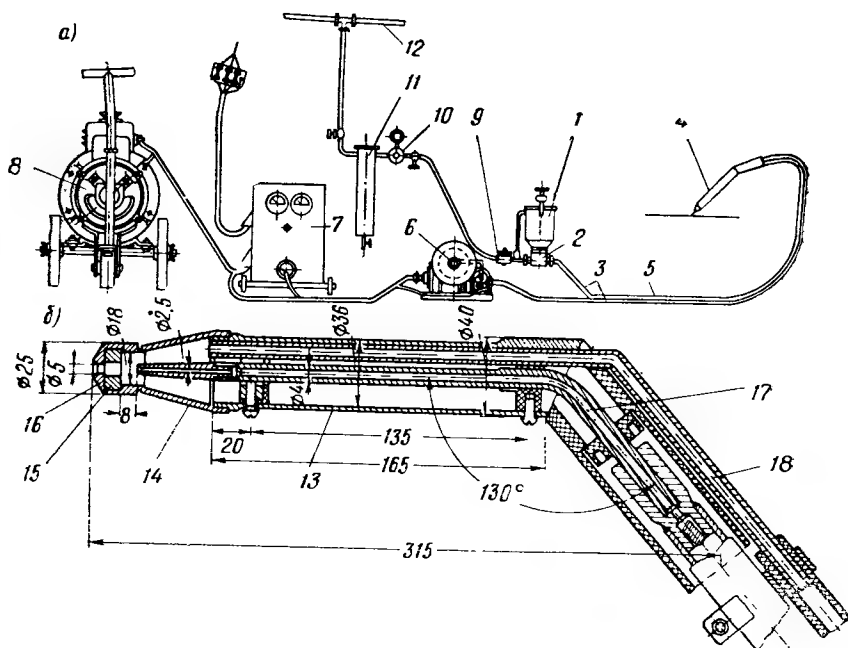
Полуавтоматическая установка для сварки с намагничивающимся флюсом
